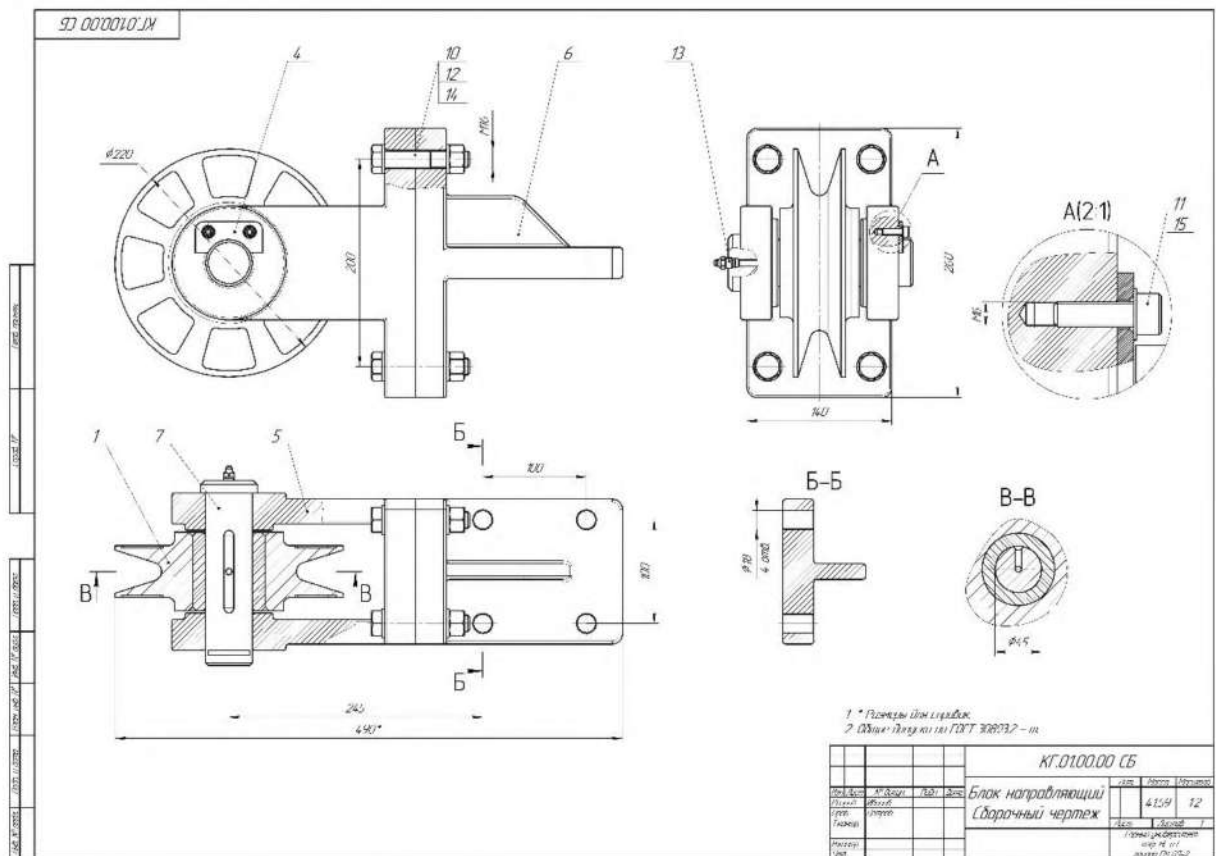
Сборочный чертеж изделия «Блок направляющий»
